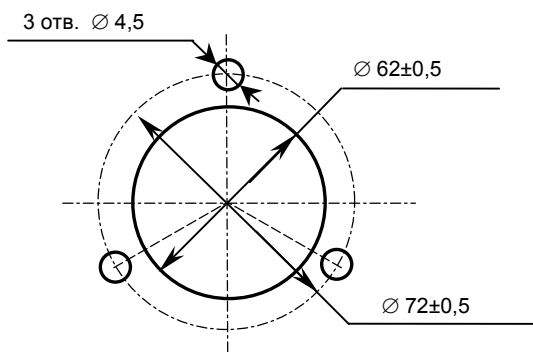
Установочные размеры штурвала LGF-12-003B-100
